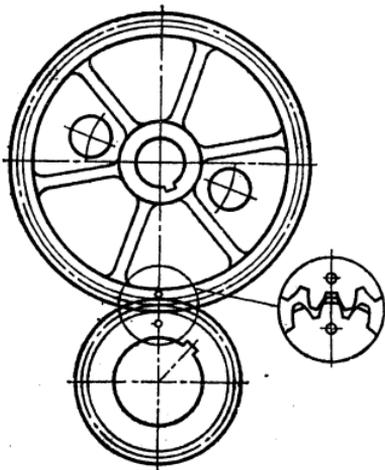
Положение меток на зубчатых колесах при установке фаз газораспределения
